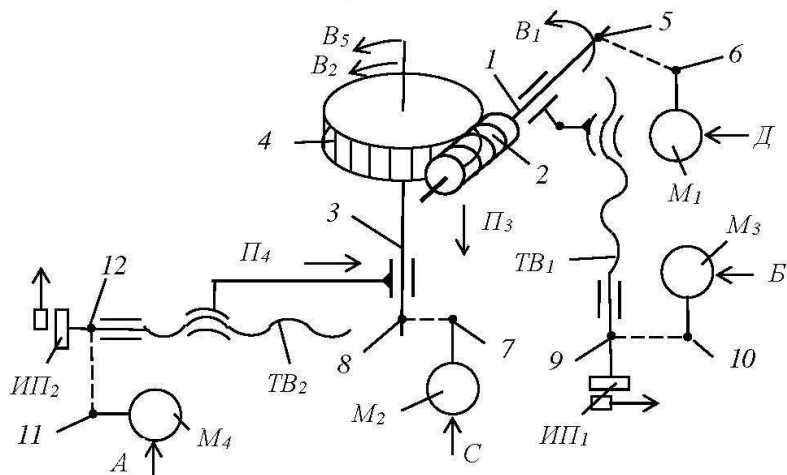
Схема приводов зубофрезерного станка для обработки колес с наклонными зубьями
